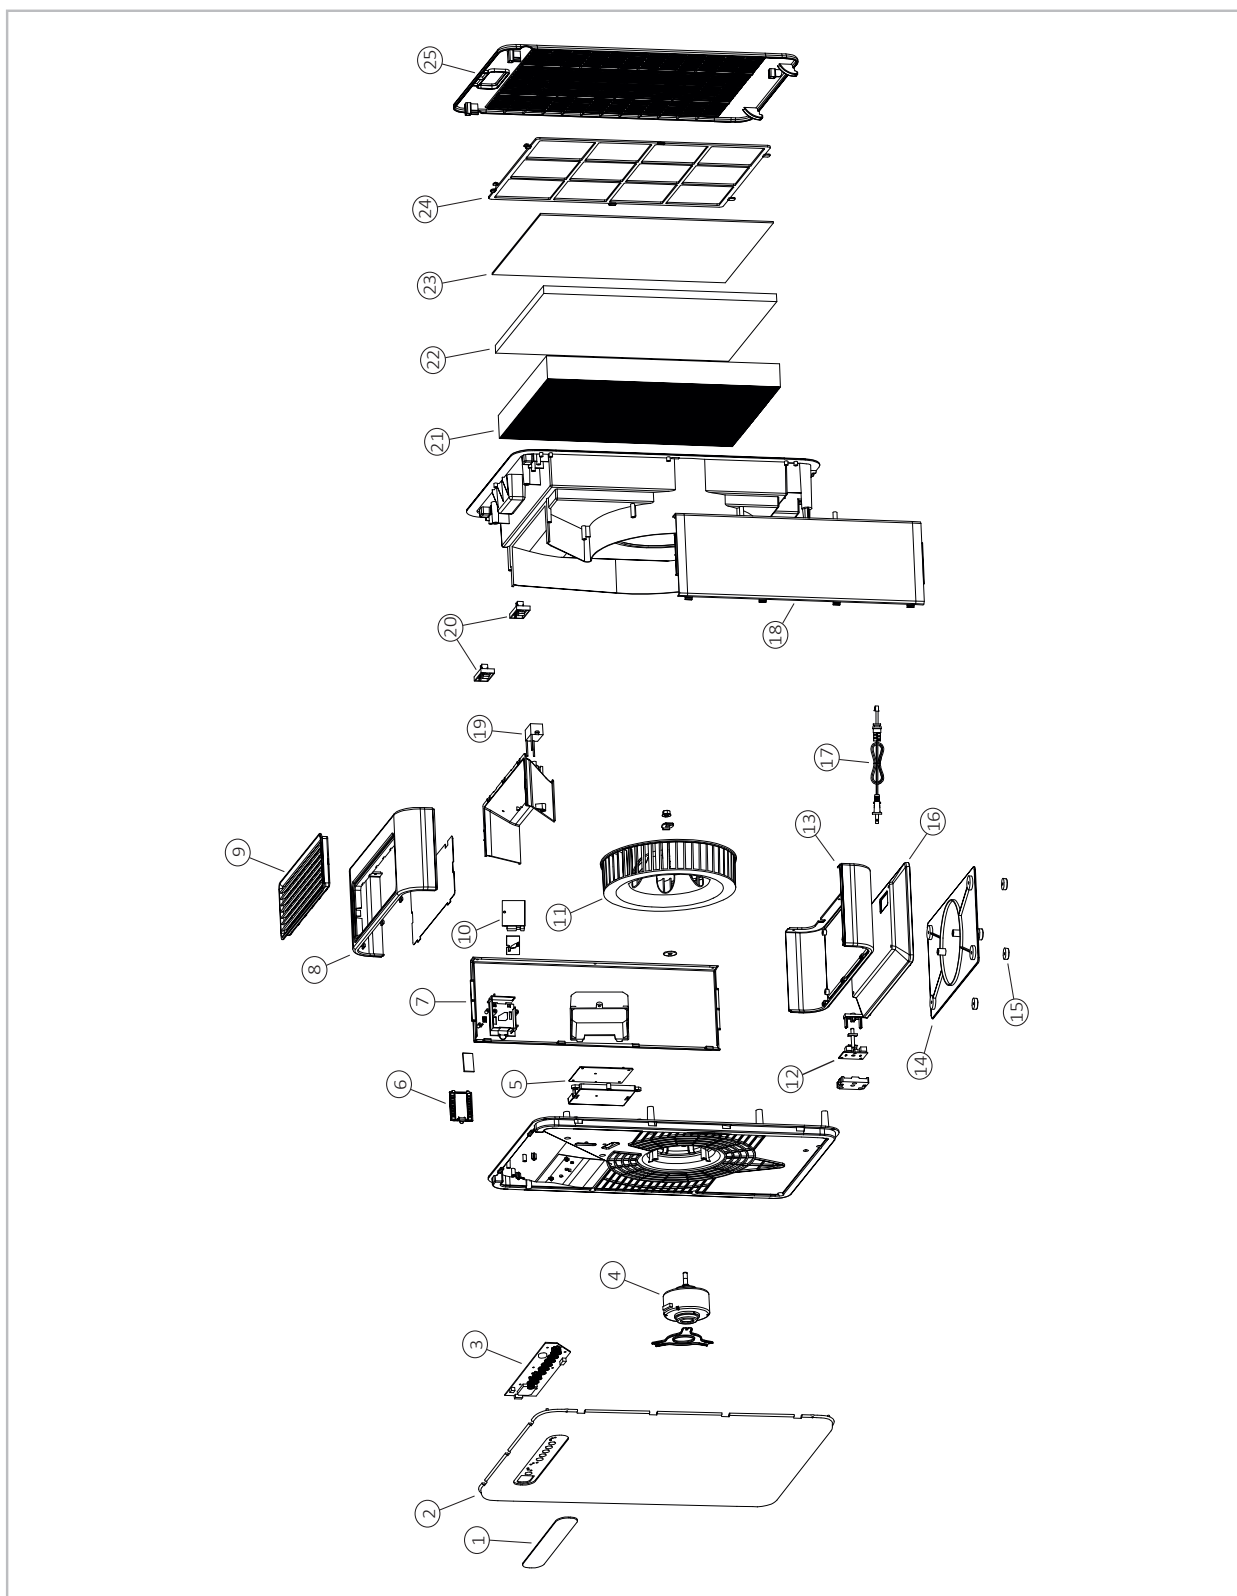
Explosionszeichnung LRM 350, LRM 500
